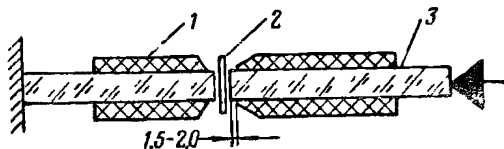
Схема сварки листов встык методом горячего лезвия:
